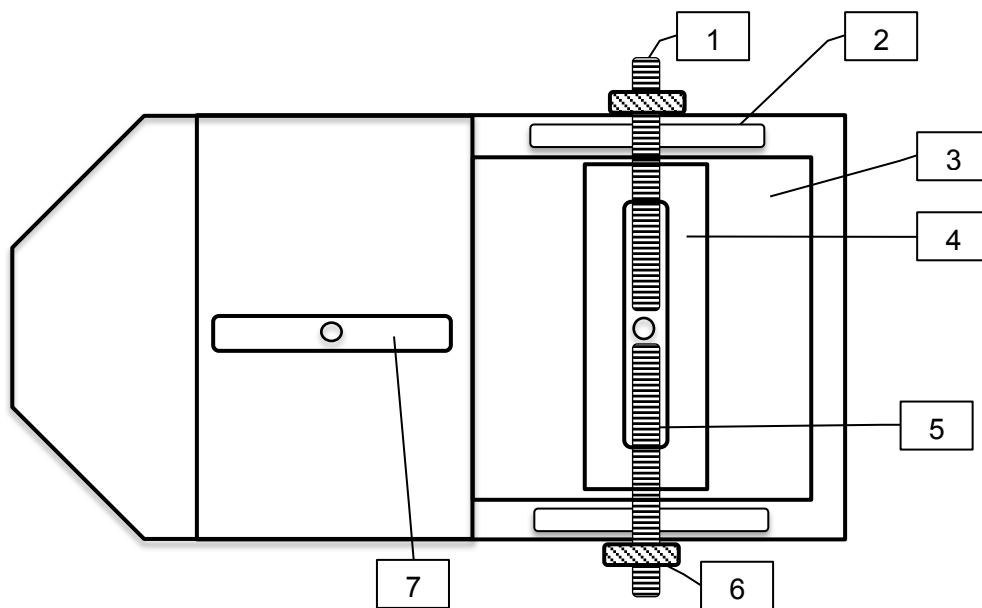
Technische Zeichnung des modifizierten proximalen Schenkels mit Bezeichnung der Bauteile. In den Ausschnitt (3) wird ein rechteckiger Kasten (4) zur Aufnahme des K-Drahtes eingesetzt. Dieser kann durch Verschieben der Gewindestangen (1) im Ausschnitt (2) entlang der Fingerachse positioniert werden. Der K-Draht kann durch ein- bzw. ausschrauben der Gewindestangen (1) ebenfalls in der palmar-dorsalen Achse in seiner Aufnahme (5) verschoben werden. Die Gewindestangen werden durch Gewindemuttern (6) in ihrer Position fixiert. Der proximale K-Draht ist in einem horizontalen Ausschnitt eingebracht (7). Dieser muss nicht fixiert werden. Er dient der zusätzlichen Stabilität am Grundglied und folgt der Einstellung entlang der Fingerachse.
